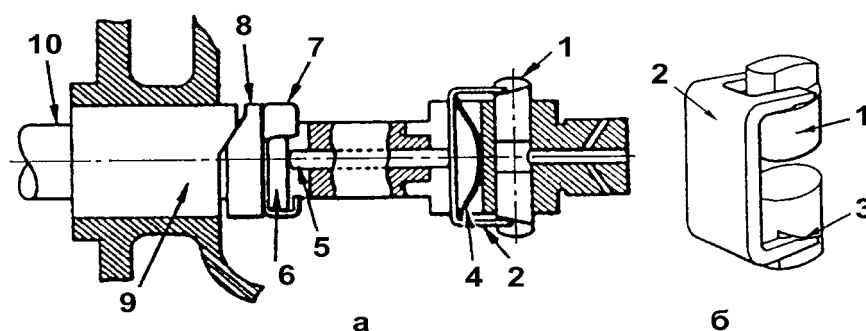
Механизм регулирования цикловой подачи в ТНВД PCF Stanadyne (а) и плунжерный узел (б): 1 - плунжер; 2 - ограничительная скоба; 3 - скосы; 4 - возвратная пружина; 5 - шток; 6 - толкатель; 7 - упорный подшипник; 8 - торцовый кулачок; 9 - поворотный регулирующий вал; 10 - приводной вал.
